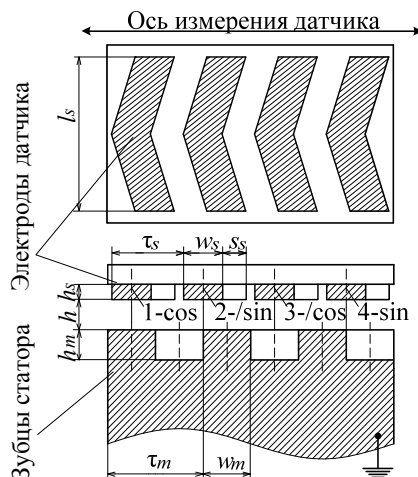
Схематичный вид элементарного ПП и зубцов статора планарного двигателя
